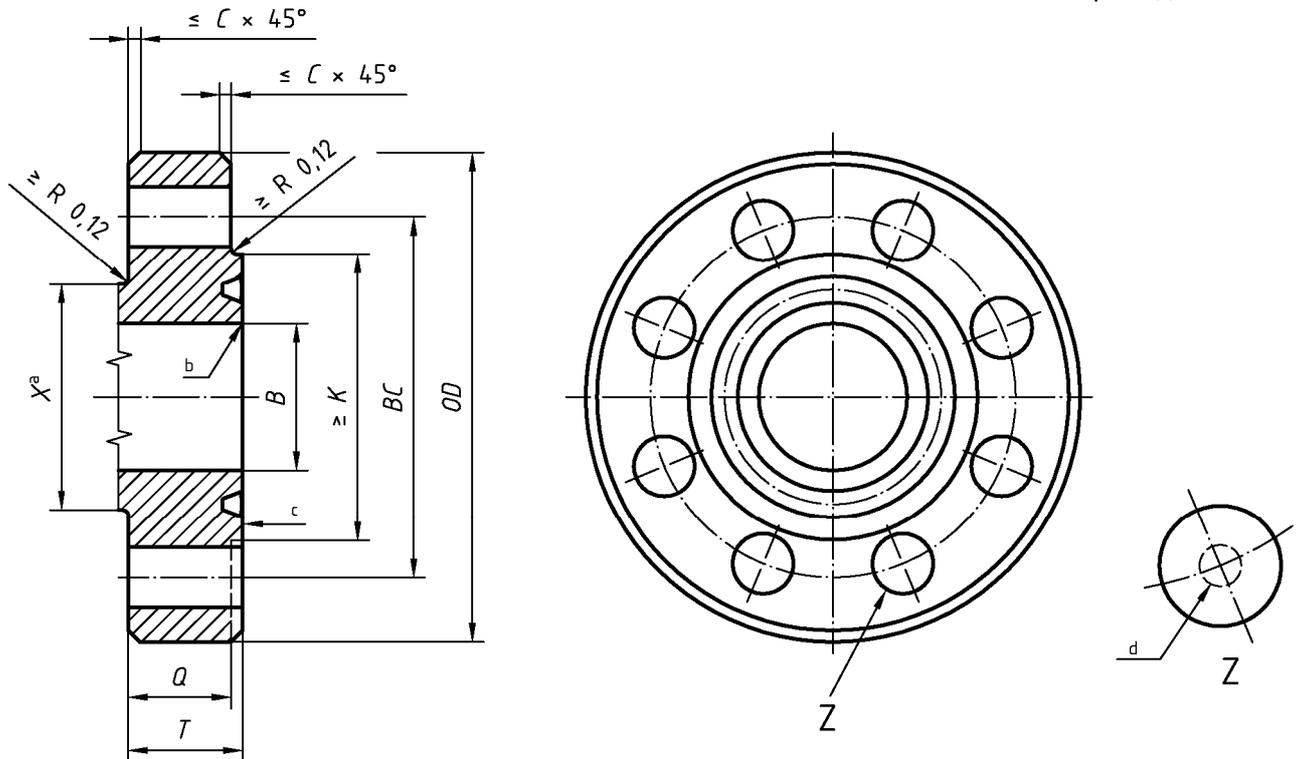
Подготовка шейки фланцев типа 6В и 6ВХ под сварку (Система единиц США)
